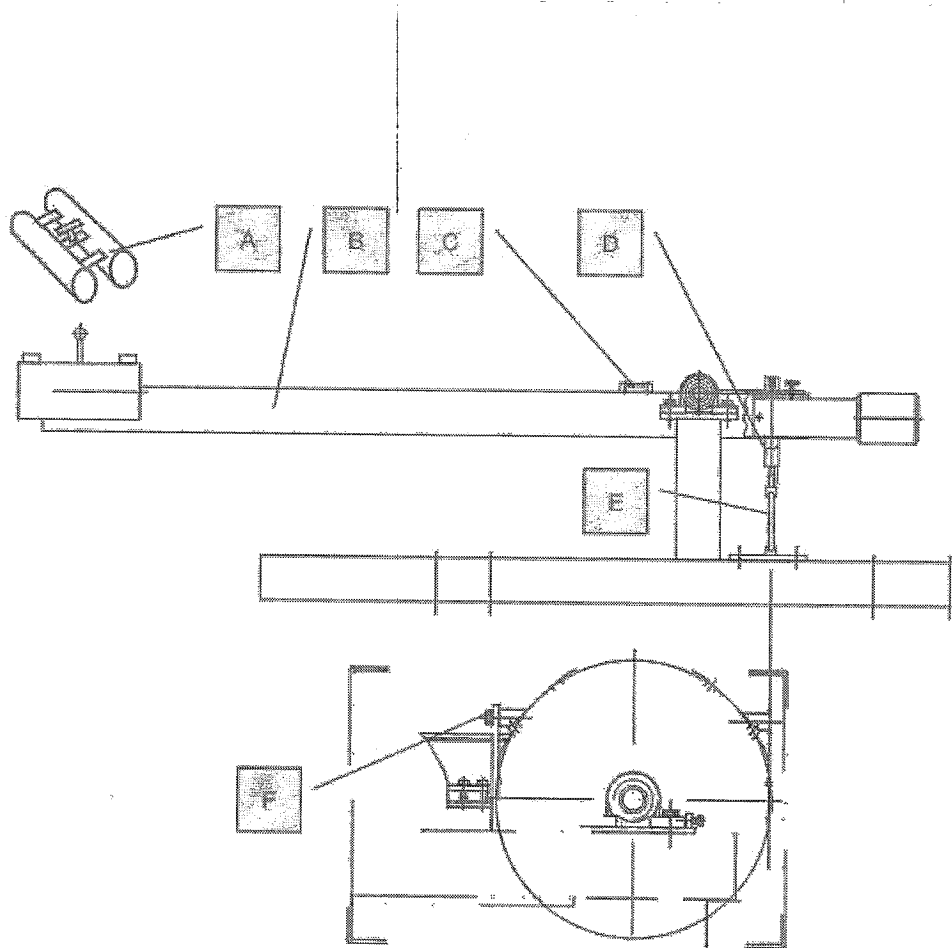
Схема установки калибровочного рычага для модификации MSR 500 и MSR 400.
